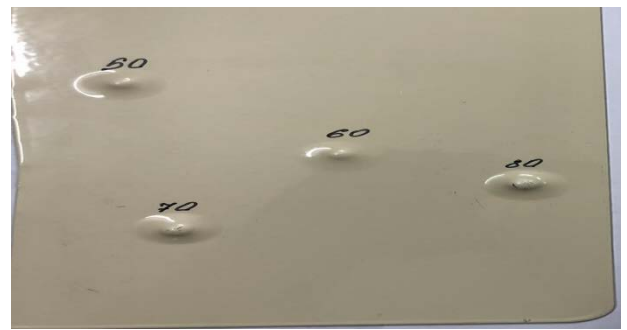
Качественная предварительная обработка поверхности изделия / детали
